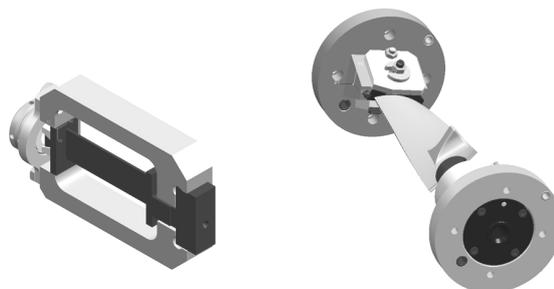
Станочные приспособления для обработки лопаток с приложением растягивающей силы
